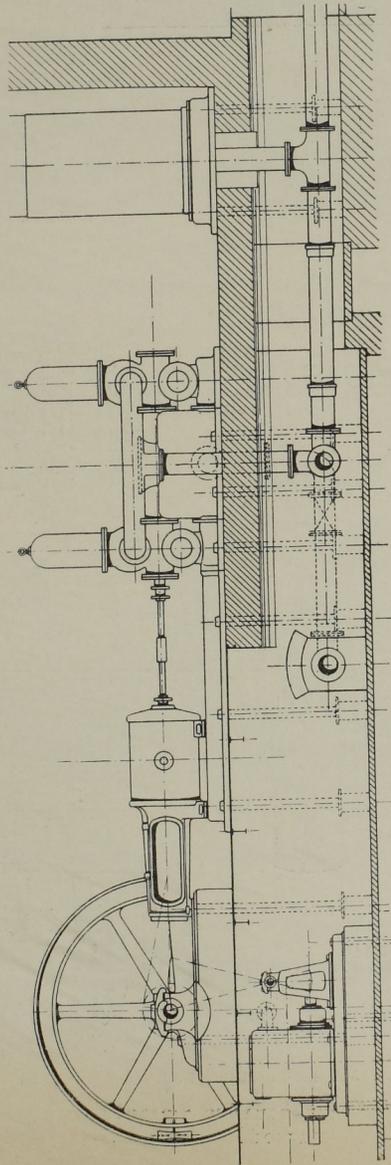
Seitenansicht der Pumpmaschinen. Masst. 1 : 75.
